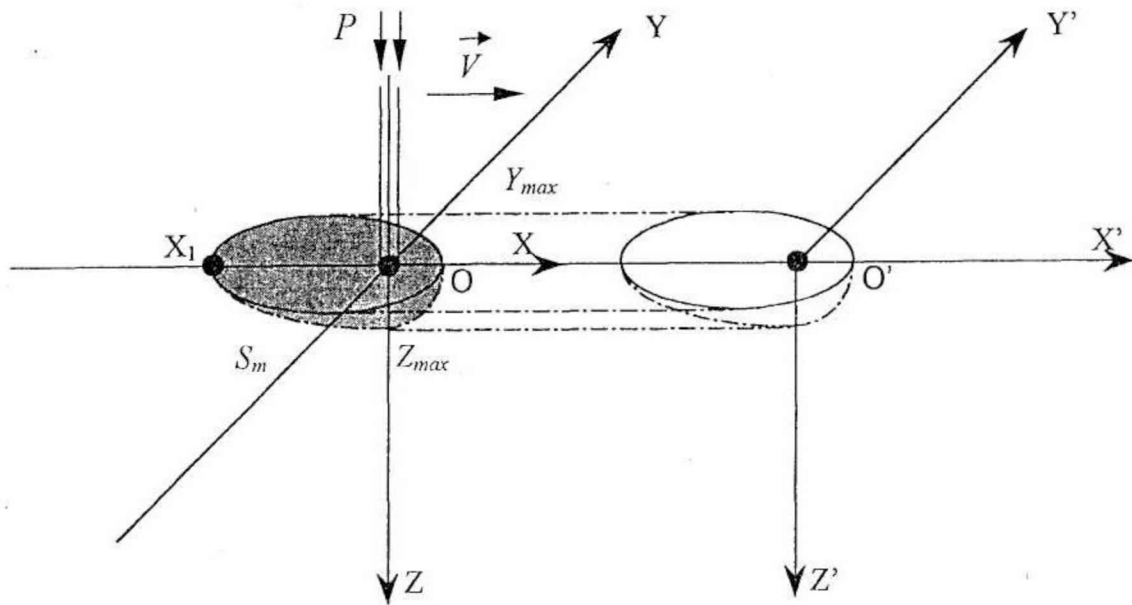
Схема лазерного наплавлення шлікерного покриття.
